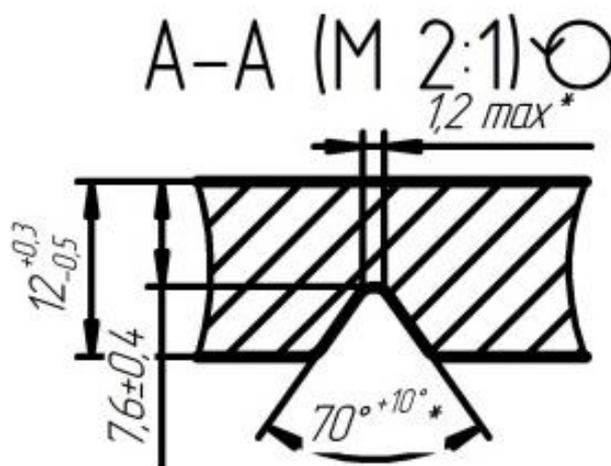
Сечение стенки детали типа «Корпус» с внутренними спиральными рифлениями (материал изделия: сталь 20 ГОСТ 1050-2013)
